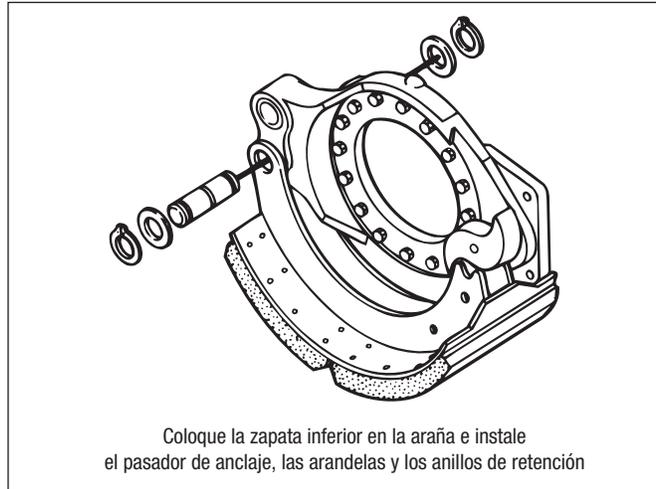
Instalación de la zapata inferior y el perno de anclaje
